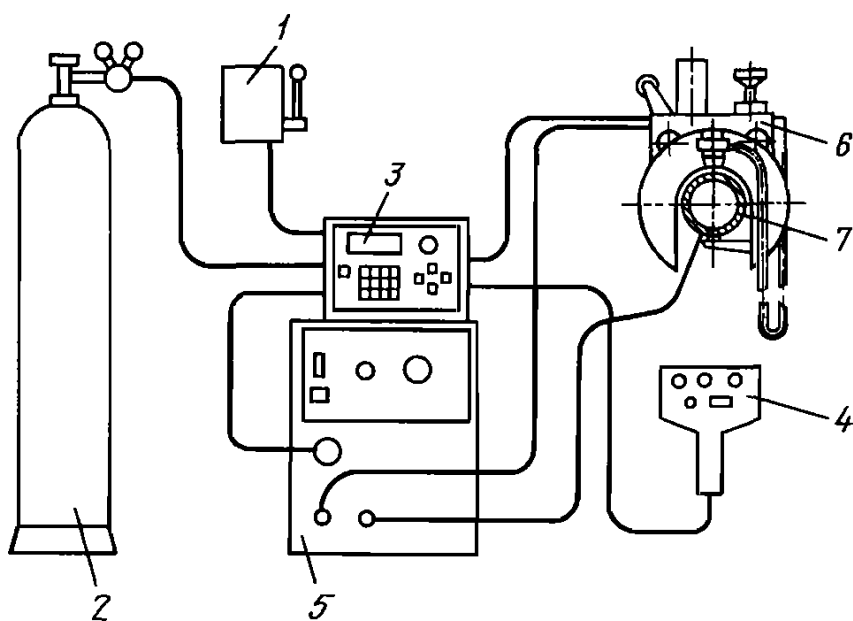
Загальний вигляд зварювального поста автоматичного аргоно-дугового зварювання неплавким електродом [5]
